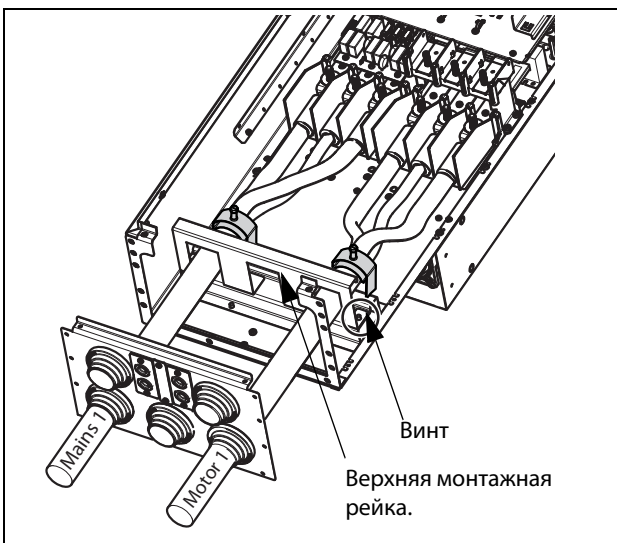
Верхняя монтажная рейка крепится над нижними кабелями.
